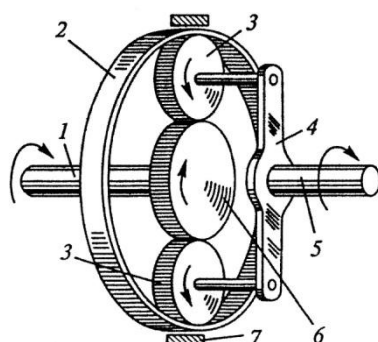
Схема планетарной передачи (1- ведущий вал с солнечной шестерней; 2 – коронная шестерня; 3 – сателлиты; 4 – водило; 5 – ведомый вал; 7 – тормоз)
